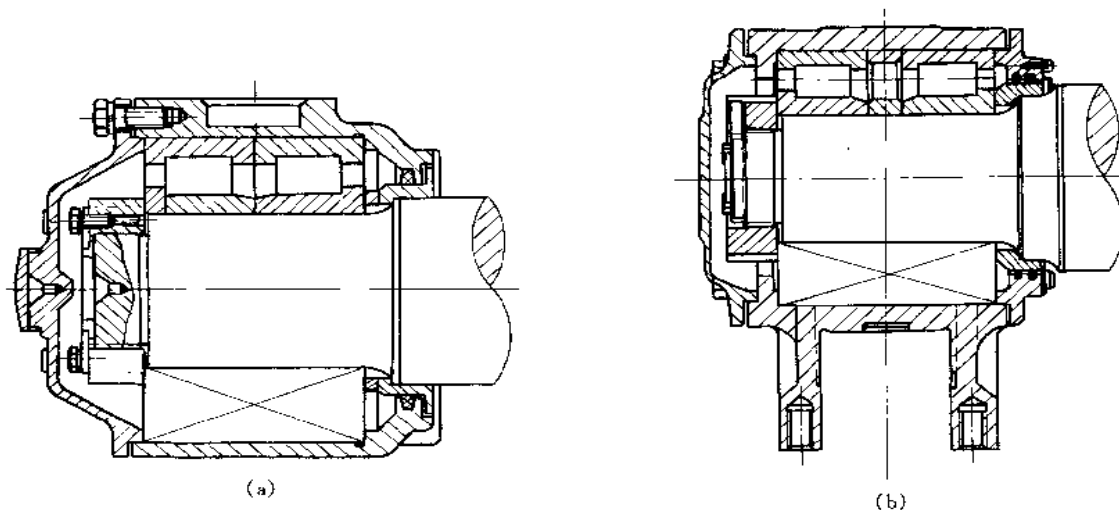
用带挡边圆柱滚子轴承做轴箱轴承
